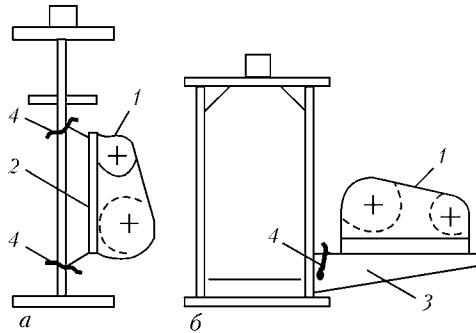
Конструктивный концентратор напряжений, образованный прикреплением рамы (а) или кронштейна (б) к листу стенки главной балки: 1 – редуктор; 2 – рама; 3 – кронштейн; 4 – трещины
